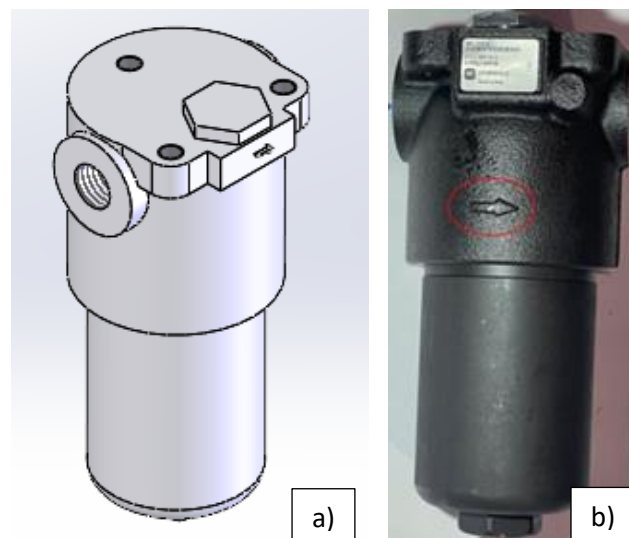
Desenho 3D (a) e imagem real do filtro do óleo (b)
